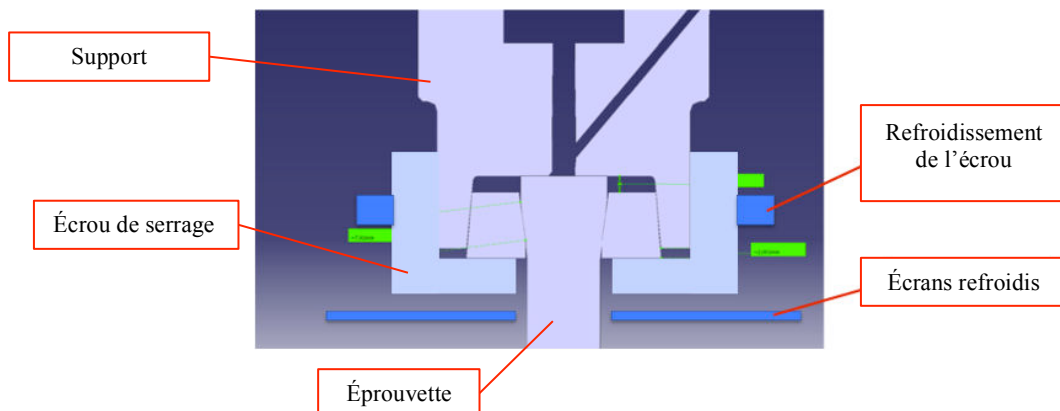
Vue en coupe de l'arrimage d'une éprouvette
